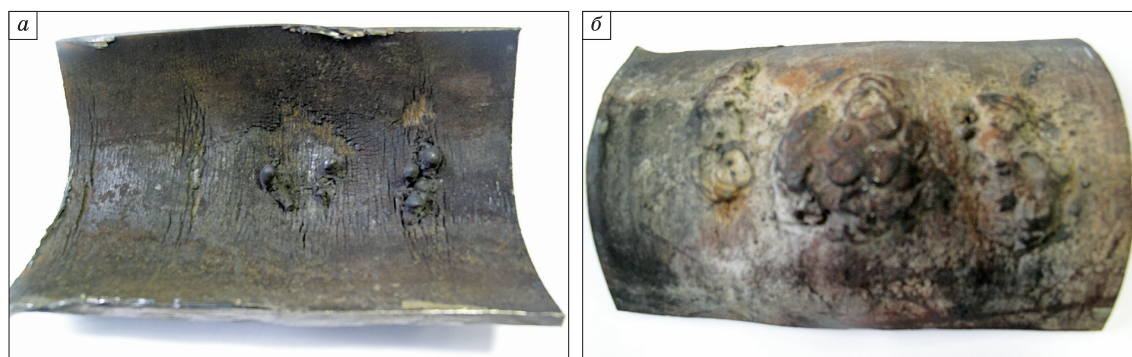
Внешний вид образца трубы поддува после ремонтной сварки:
